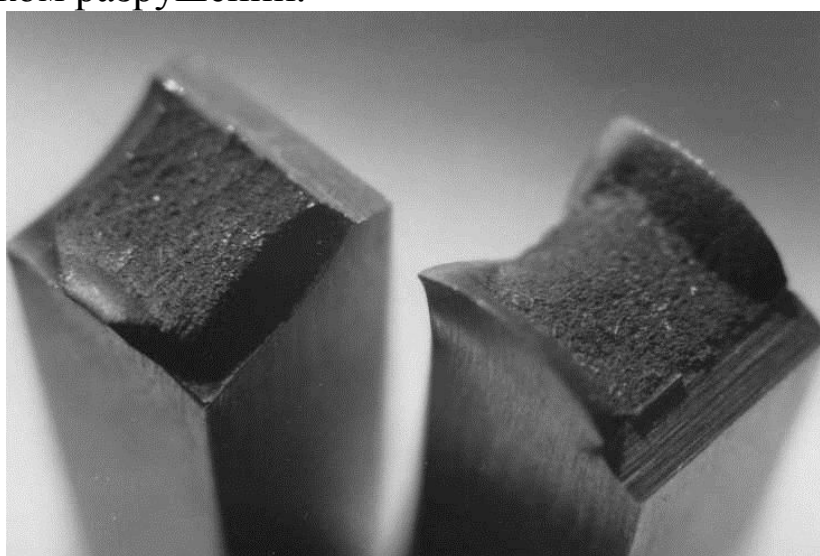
Внешний вид вязкого излома аустенитной стали
